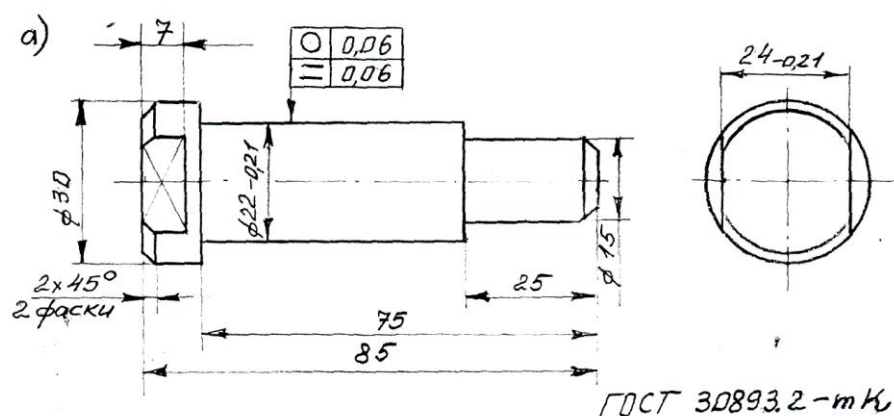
Обозначение на чертеже детали допусков размеров, формы и расположения поверхностей:
